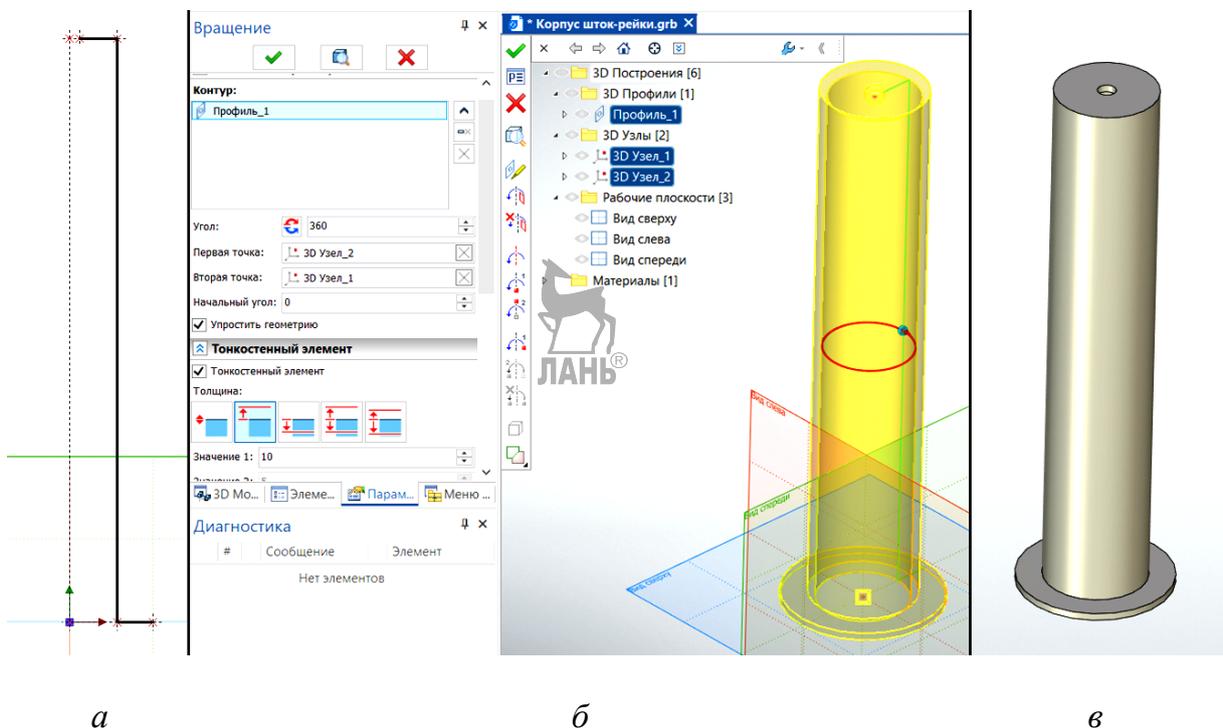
Построение 3D-модели корпуса шток-рейки операцией вращения:
